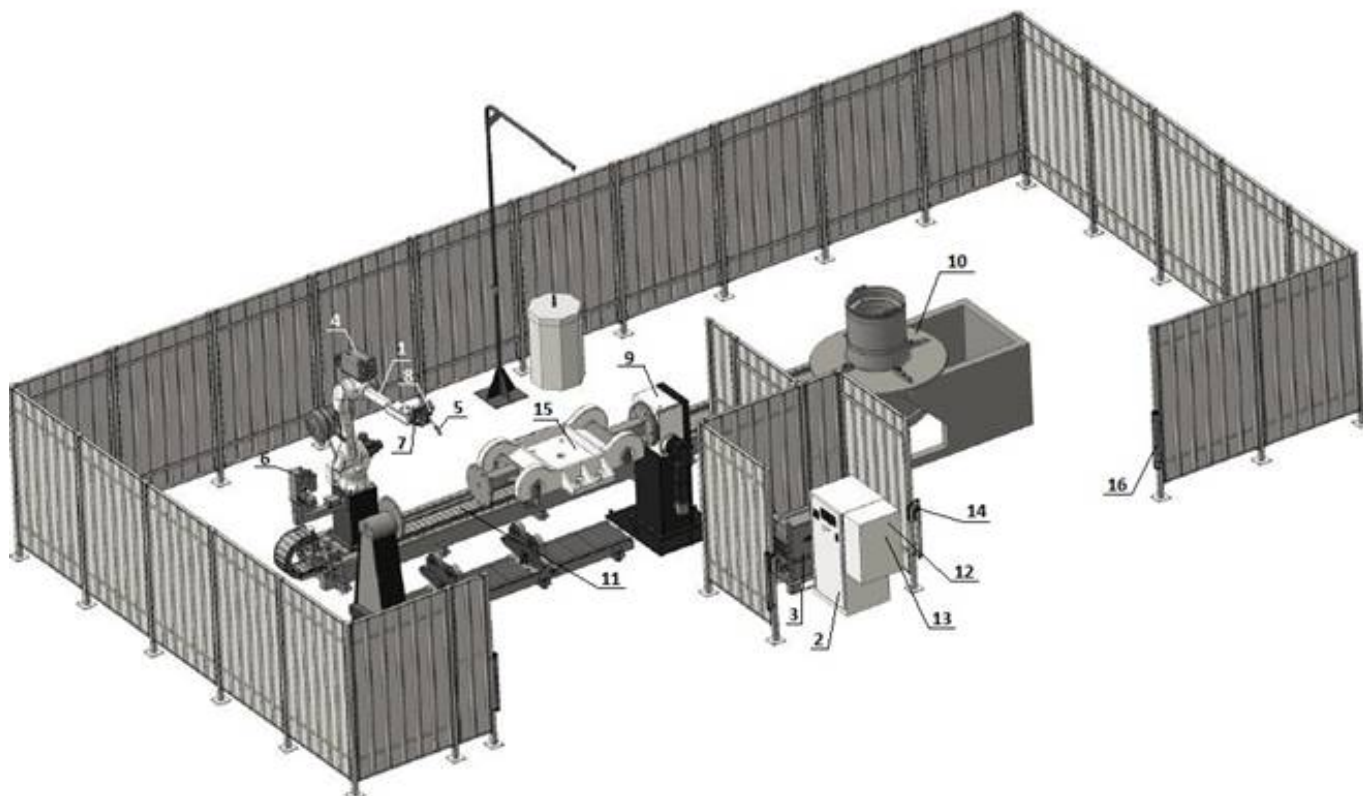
Робототехнический комплекс для сварки рамы - тележки шахтной вагонетки и сварки дисков грузоподъемных машин
